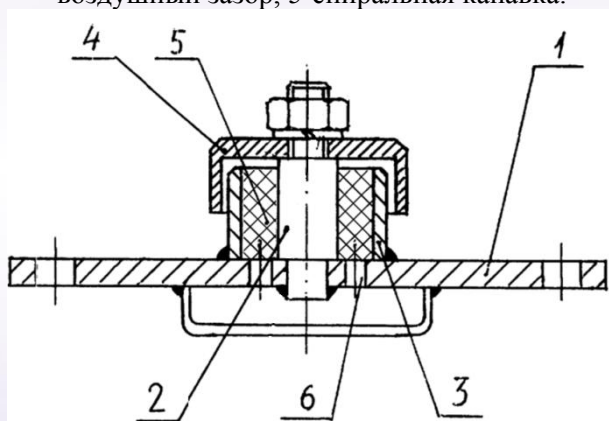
Отдушина с фильтрующим элементом: 1-корпус, 2-стойка, 3-цилиндрическая гильза, 4-крышка, 5-фильтр,
